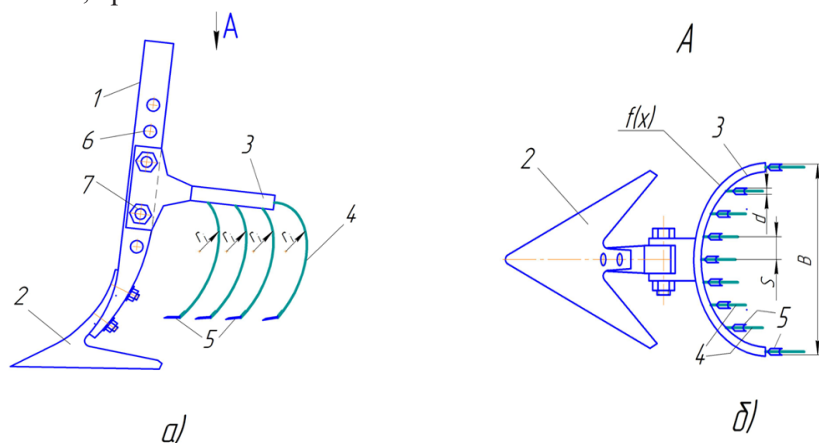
Рабочий орган культиватора с верхнерыхлительными наральниками на упругих граблинах: а) вид сбоку, б) вид сверху
